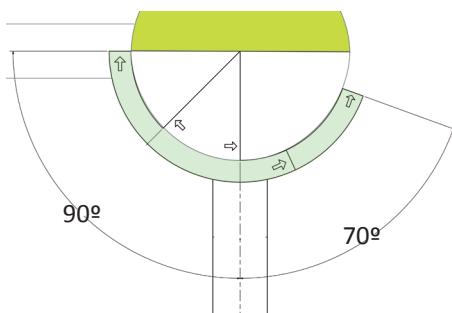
Ensamblaje rodilla fuerzas ligeras
